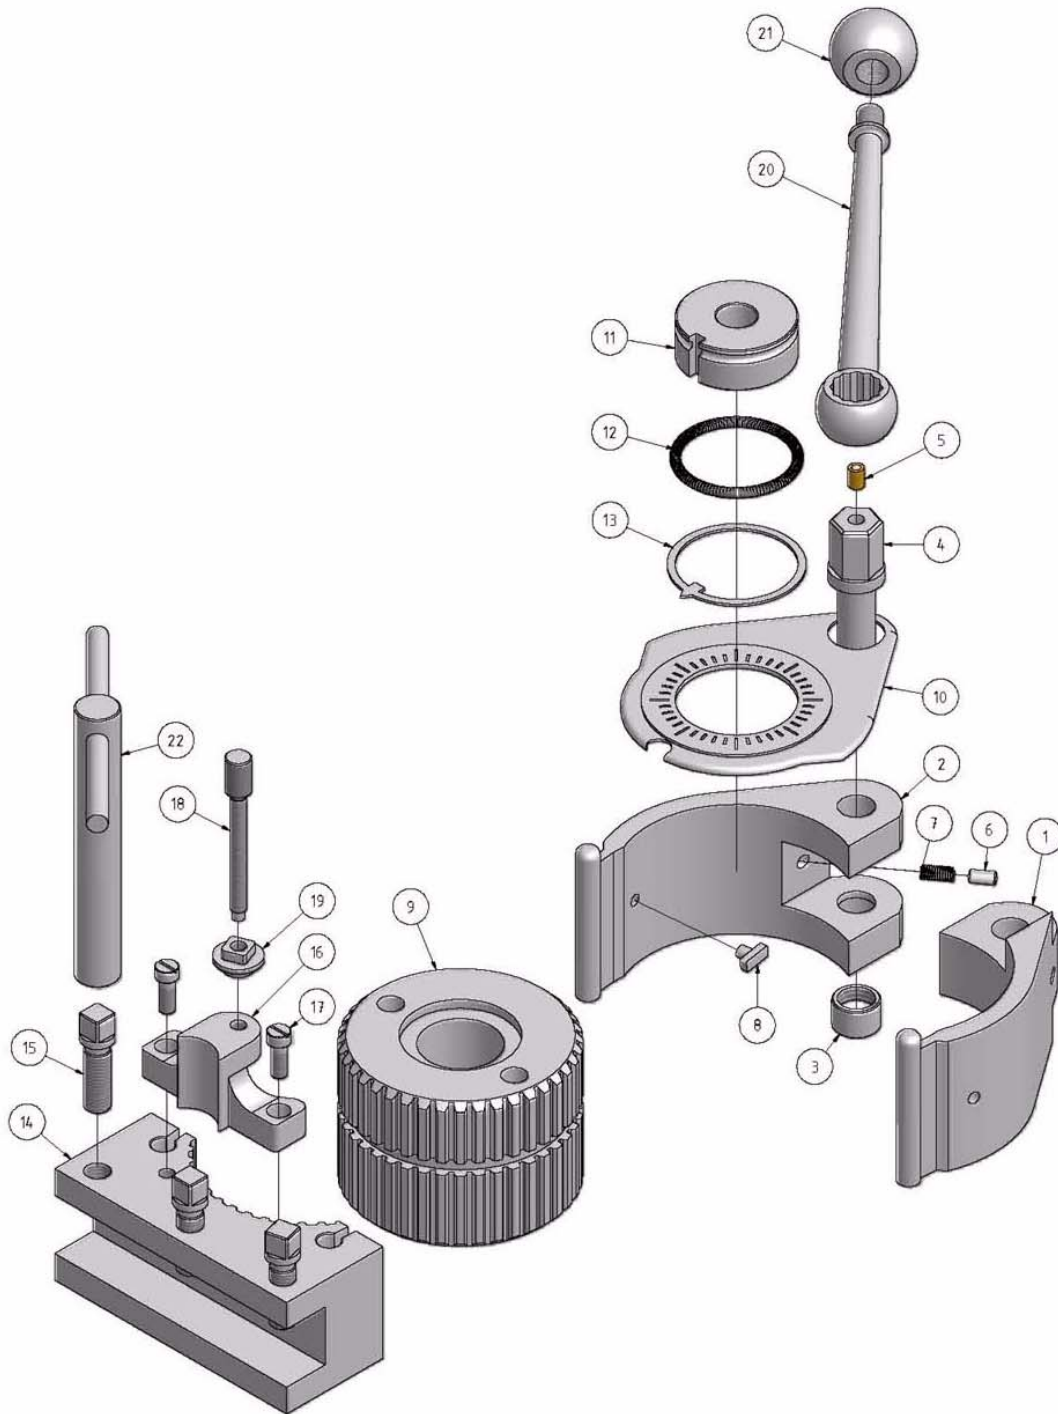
Ersatzteilzeichnung - Drawing spare parts
